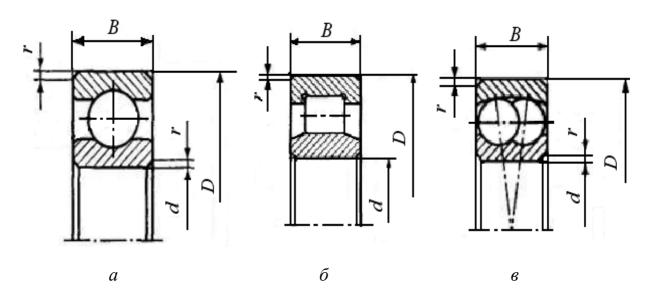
Присоединительные размеры подшипника a — подшипник шариковый радиальный; δ — подшипник роликовый радиальный; ϵ — подшипник радиальный сферический двухрядный
